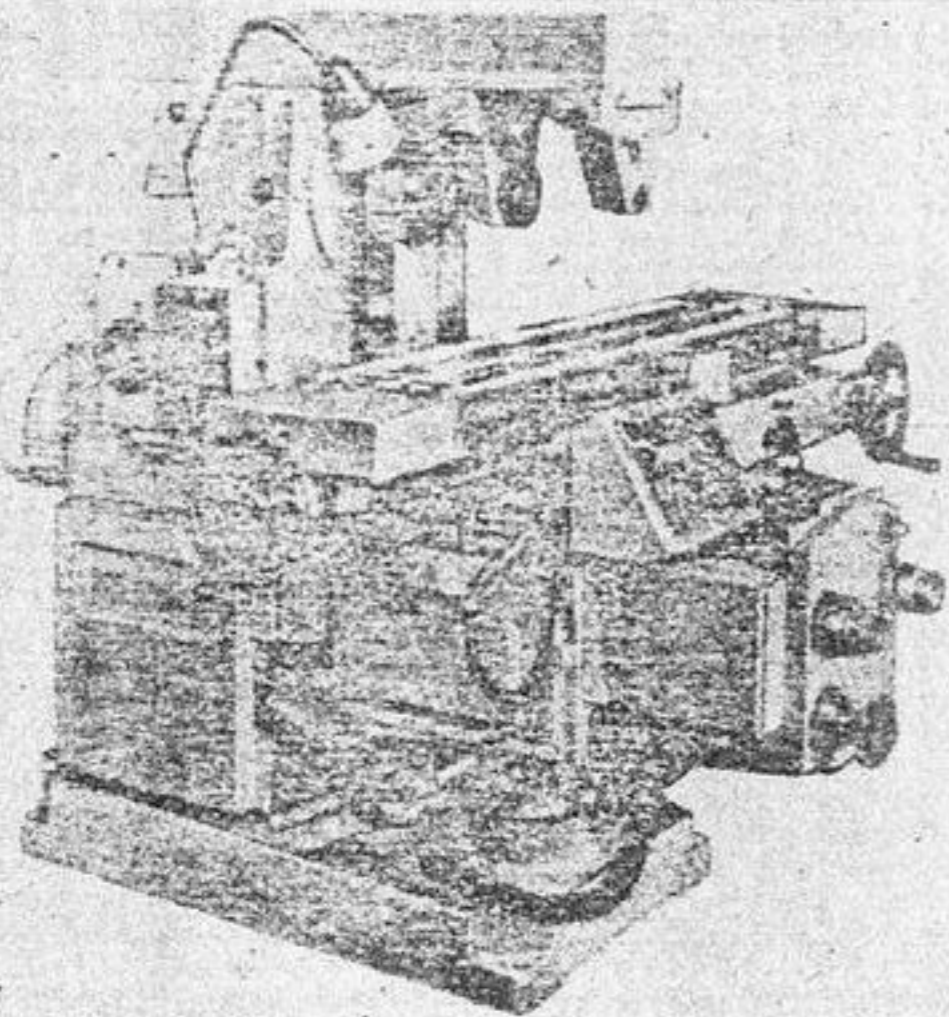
Горизонтальный консольно-фрезерный станок 6Т82Г-29
